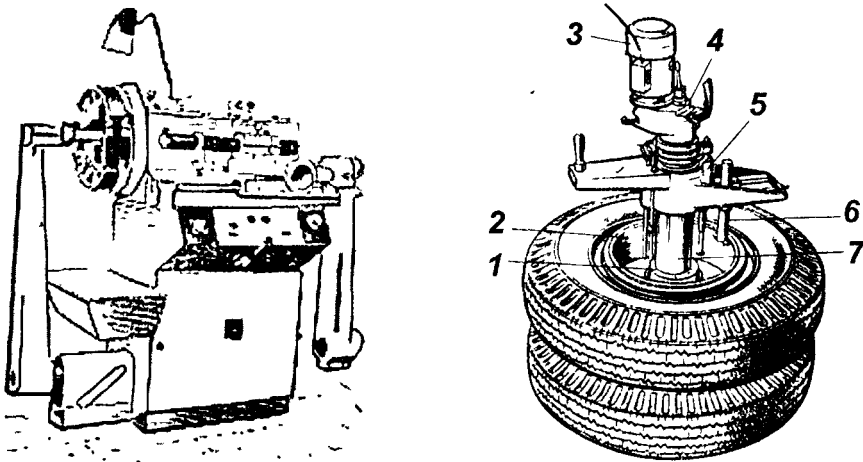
Верстати для розточування зношених робочих поверхонь гальмівних барабанів: 1 – маточина колеса; 2 – гальмівний барабан; 3 – електродвигун; 4 – редуктор; 5 – каретка; 6 – різець; 7 – шпиндель
